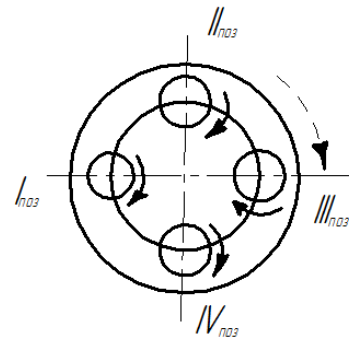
Позиції, які займаються по черзі заготовкою при обробці на 4-шпиндельному токарному напівавтоматі
